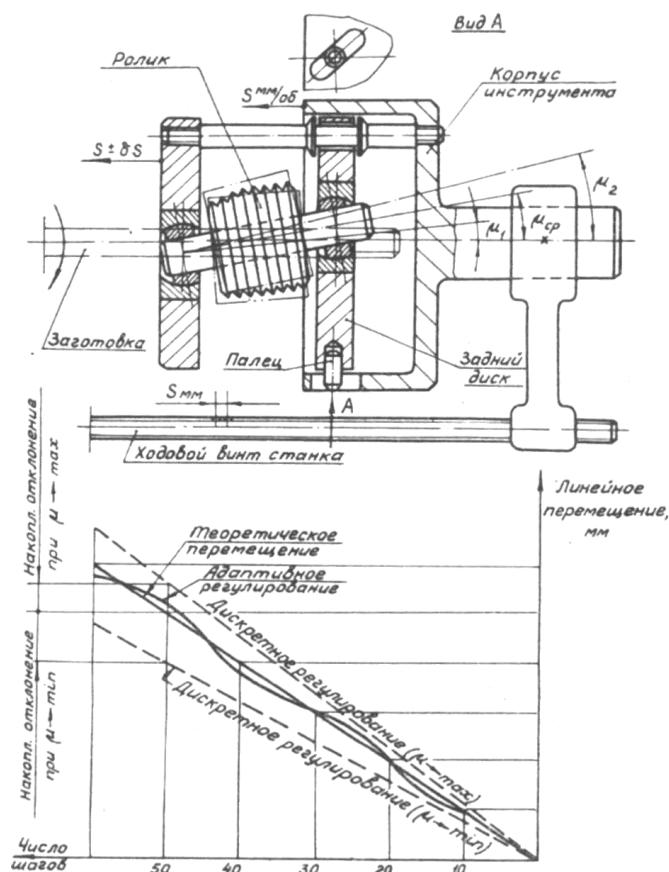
Вариант обработки точных по шагу винтов на токарном станке осевой резбонакатной головкой с адаптивным управлением геометрией инструмента.
